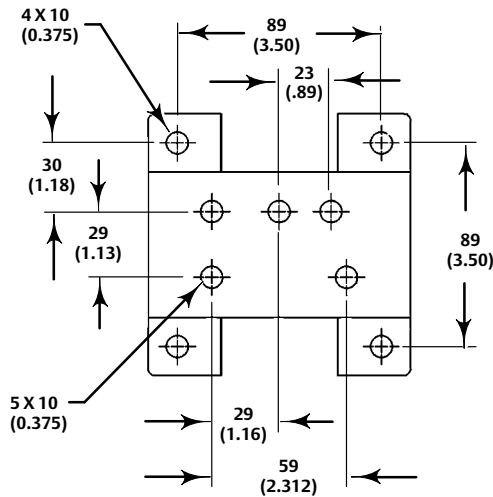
Montaggio del trasduttore tipico con staffa di montaggio universale
